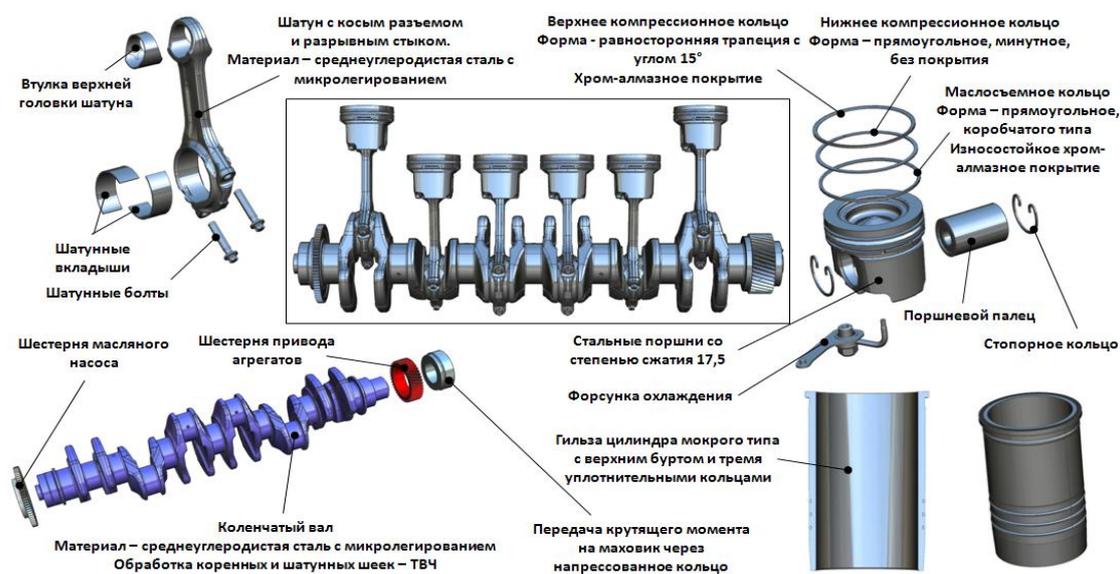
Цилиндропоршневая группа двигателя КАМАЗ Р6
